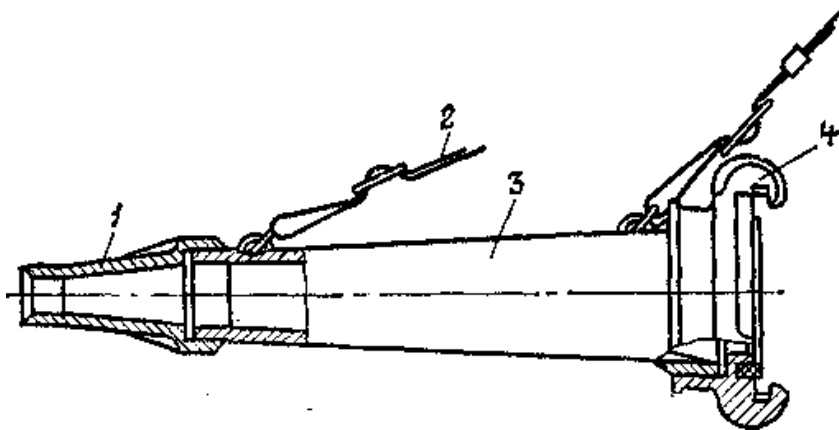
Принципова схема будови ручного пожежного ствола РС-70:
